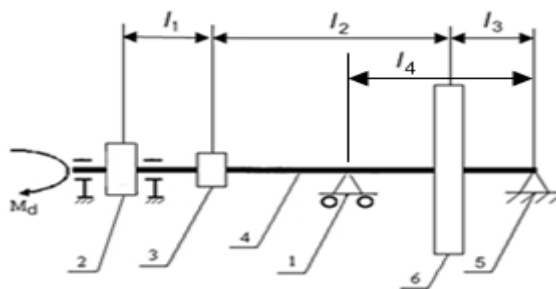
Компоновка ротора осевого вентилятора: 1, 5 – подшипниковые опоры, 2 – электродвигатель, 3 – муфта, 4 – трансмиссионный вал, 6 – рабочее колесо
